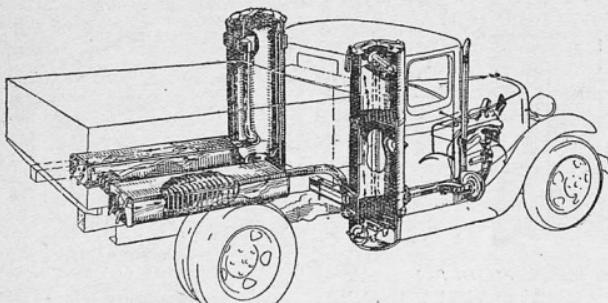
Расположение агрегатов газогенераторной установки НАТИ Г-14 на шасси автомобиля
